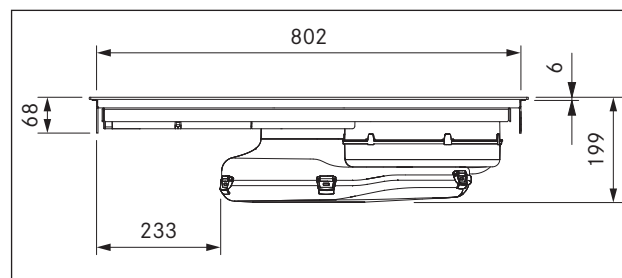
PUXA dimensioni apparecchio vista frontale
